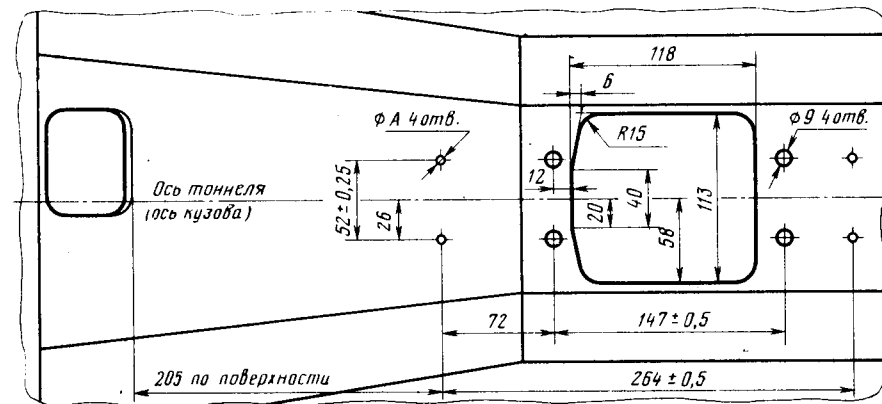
Окно для напольного механизма управления коробкой передач (вид сверху):
